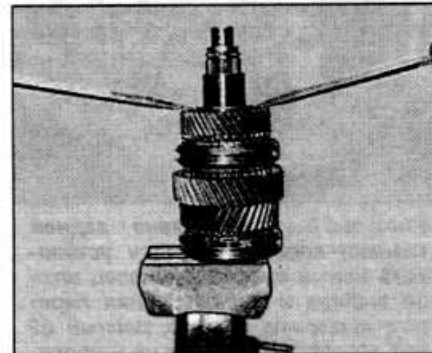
Снятие втулки игольчатого подшипника шестерни III передачи
